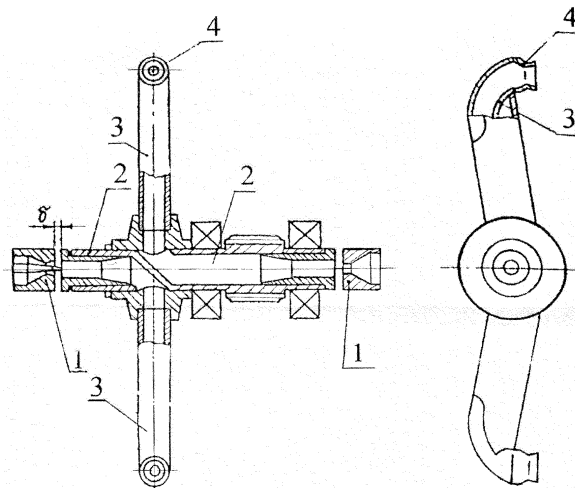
Конструктивна схема реверсивної струминно-реактивної турбіни:
